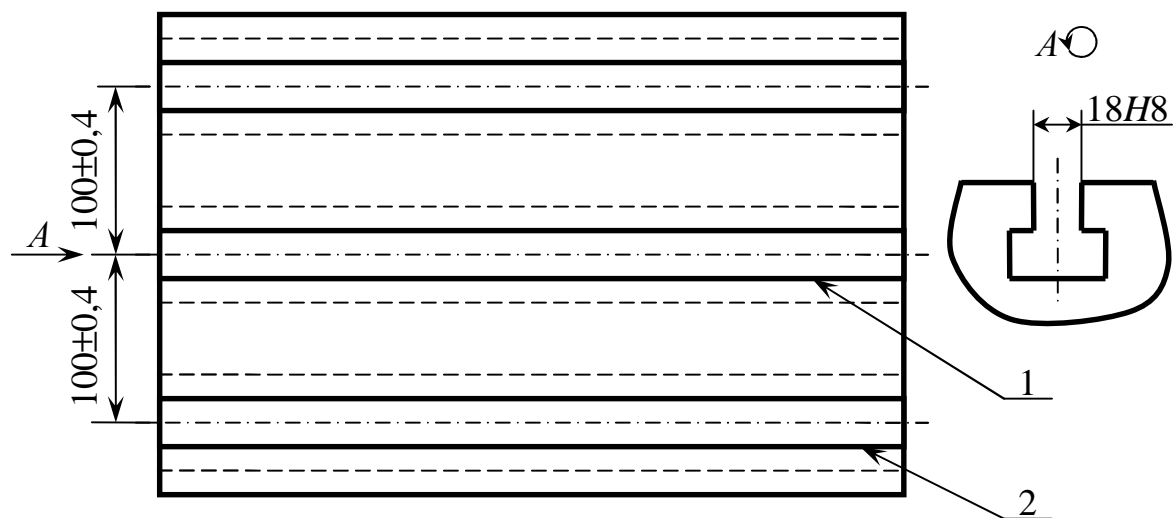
Конструкция стола станка ГФ2171С5 (вид сверху)
